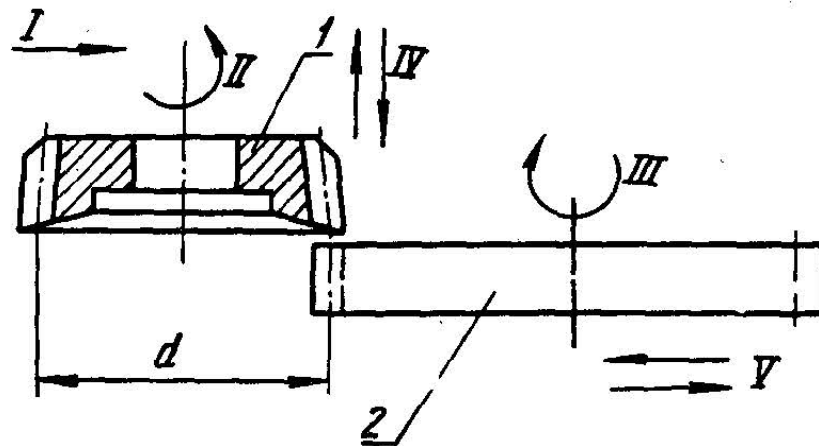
Схема нарізання зубчатого колеса довбачем:
